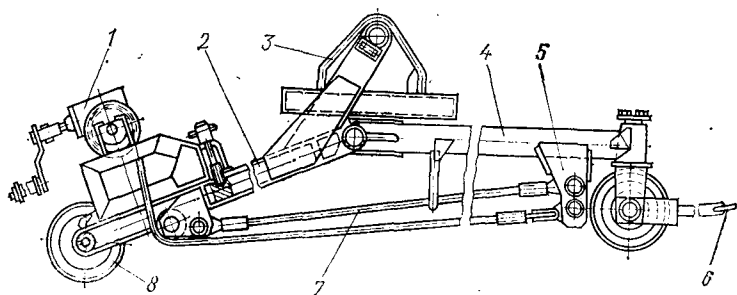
Тележка подъемно-транспортная для снятия и транспортировки коробки перемены передач автомобилей
